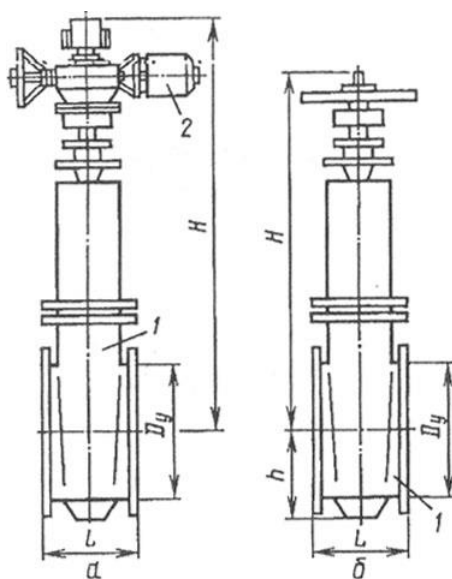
Клиновая задвижка с невыдвижным шпинделем фланцевая укороченной длины: а – с электроприводом; б – с ручным управлением; 1 – корпус; 2 – электропривод
